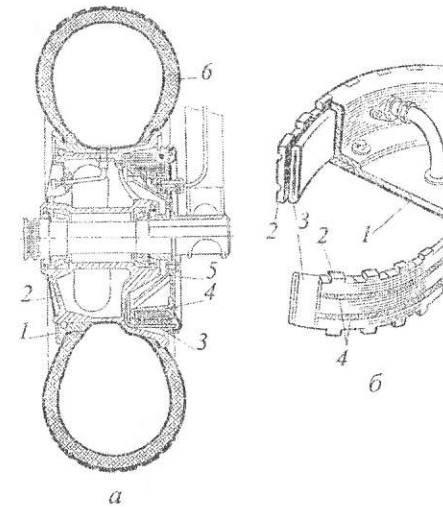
Конструкція колеса шасі: 1 – барабан; 2 – реборда; 3 – гальмівна сорочка; 4 – гальмо; 5 – маточина; 6 – пневматик камерного гальма; б: 1 – корпус гальма; 2 – гальмівна колодка; 3 – гумова камера; 4 – пружина
